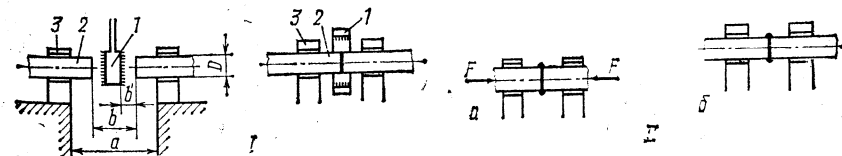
Принцип сварки: а — открытая сварка; б — закрытая сварка; 1 — перед сваркой; 1' — после сварки; 1 — двухпламенная горелка или кольцевая горелка; 2 — свариваемое изделие; 3 — зажимы
